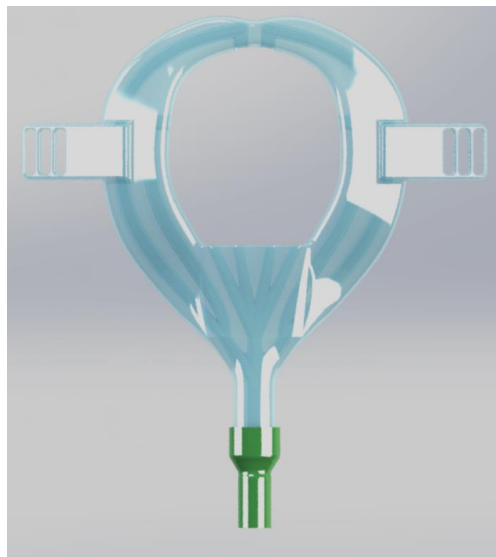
Configuración geométrica de alternativa de producto para manufactura por “soplado”, no requiere alta complejidad de diseño de molde y se reduce el costo de manufactura, es un prototipo desechable.
